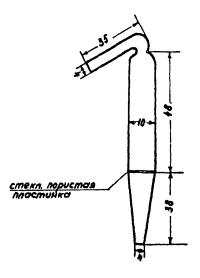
Рис. I. Стенлянная трубка с пористой пластині юй для отбора проб воздужа
